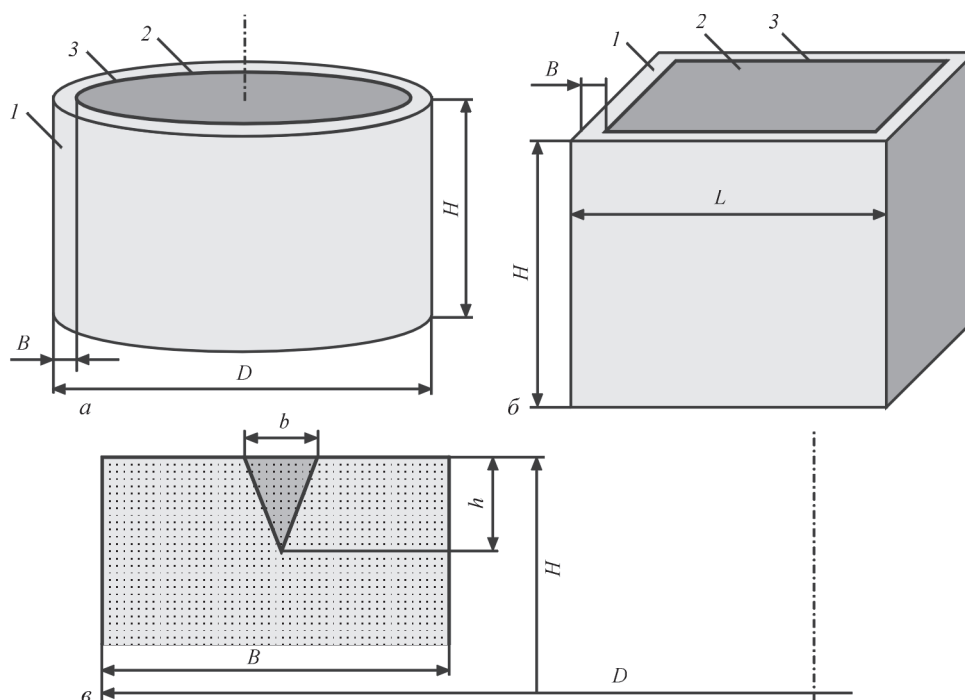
Геометричні параметри деталей, що зварюються, і лазерного провару (темна трикутна ділянка): 1 – корпус; 2 – фланець, що приварюється; 3 – зварний шов
